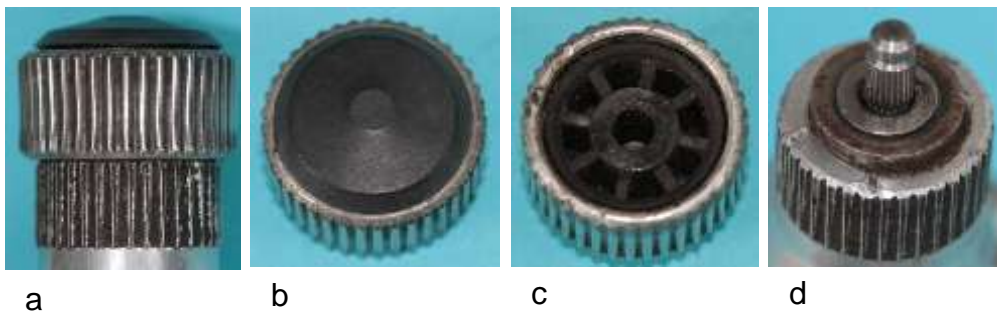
Reibrad mit Stahlbandage: a) Auf dem Lagerhals eingepprägter Kragen und Reibrad, b) Obere Reibradfläche, c) Unterseite mit Wellenbohrung, d) Wellenende mit Kragen
